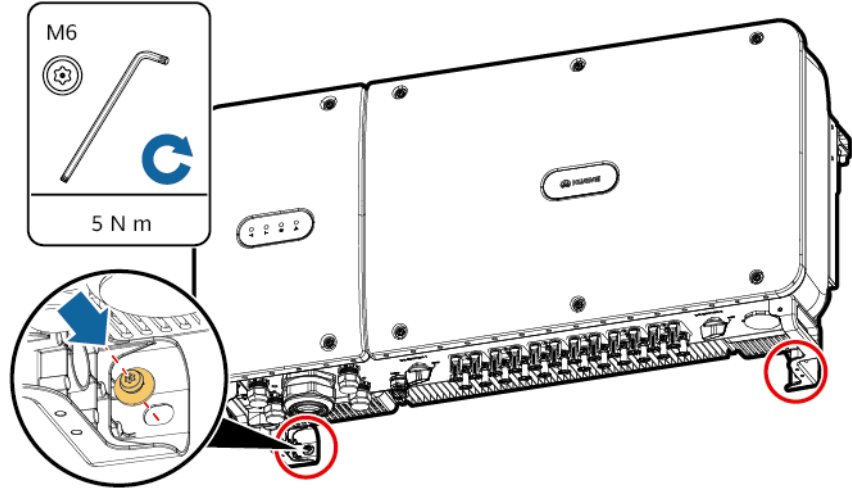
SUN2000'i montaj braketine montajlayın.
